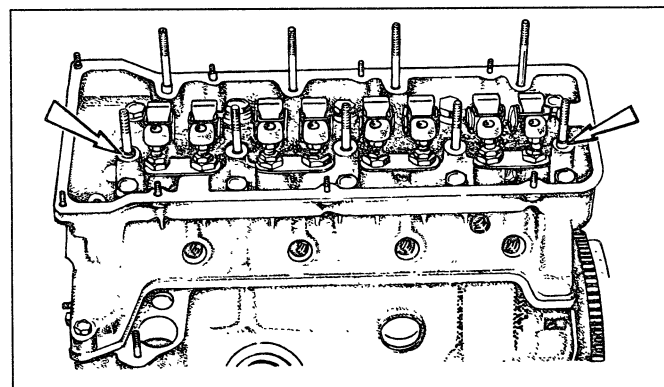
Установочные втулки для корпуса подшипников распределительного вала
